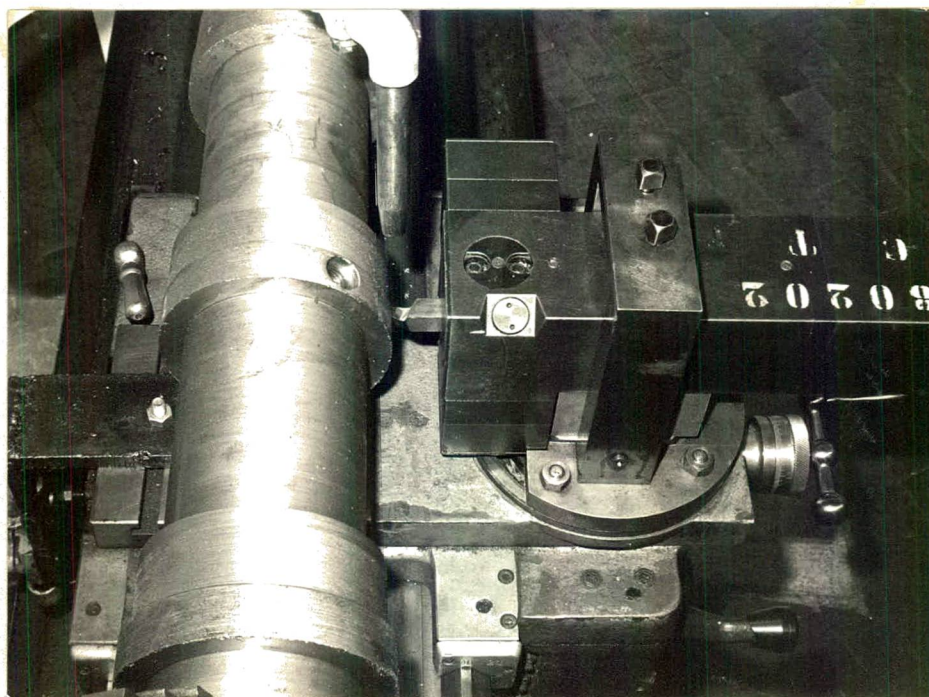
Detalhe da usinagem através do dinamômetro Fischer.
